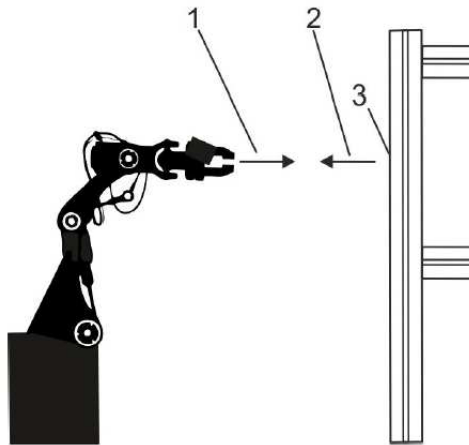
Beispiel: Roboter mit Schienenengerüst zur Befestigung des Montageadapters
